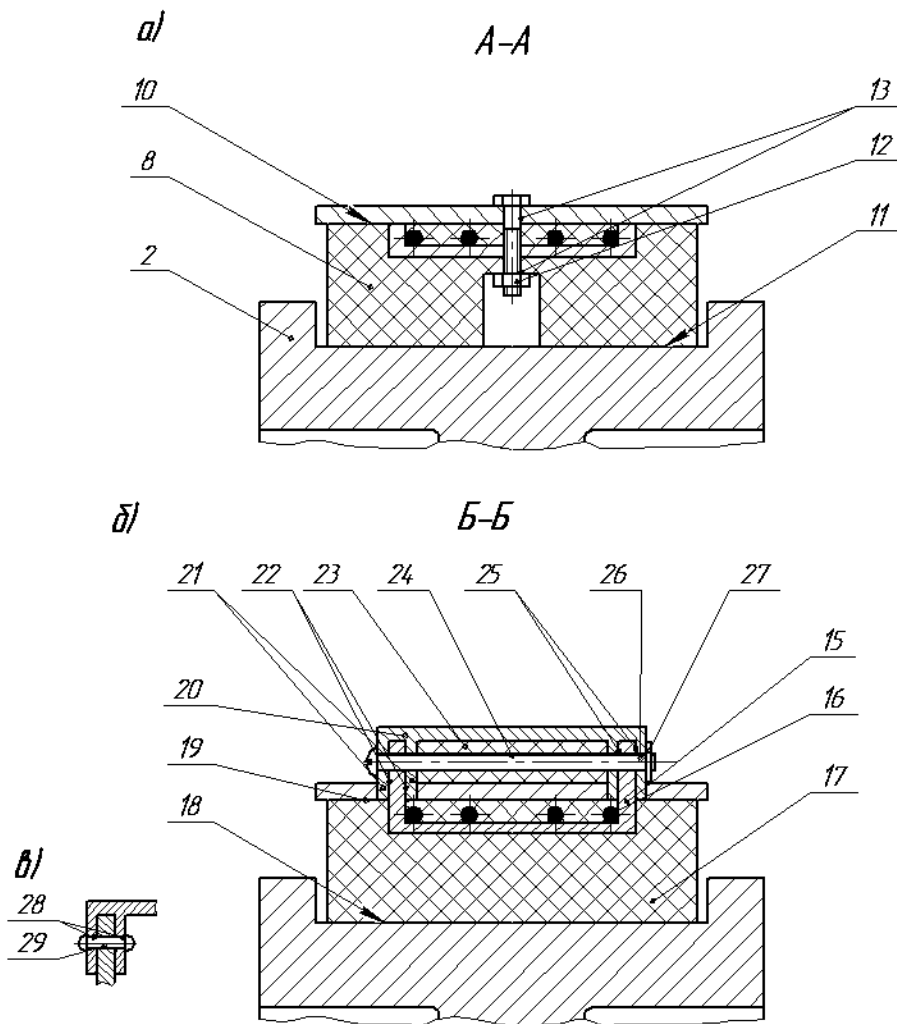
Поперечні розрізи фрикційного вузла гальма з нерухомою (а) та з рухомою (б) фрикційними накладками і кріплення пластини останньої до накидного кожуха (в)
